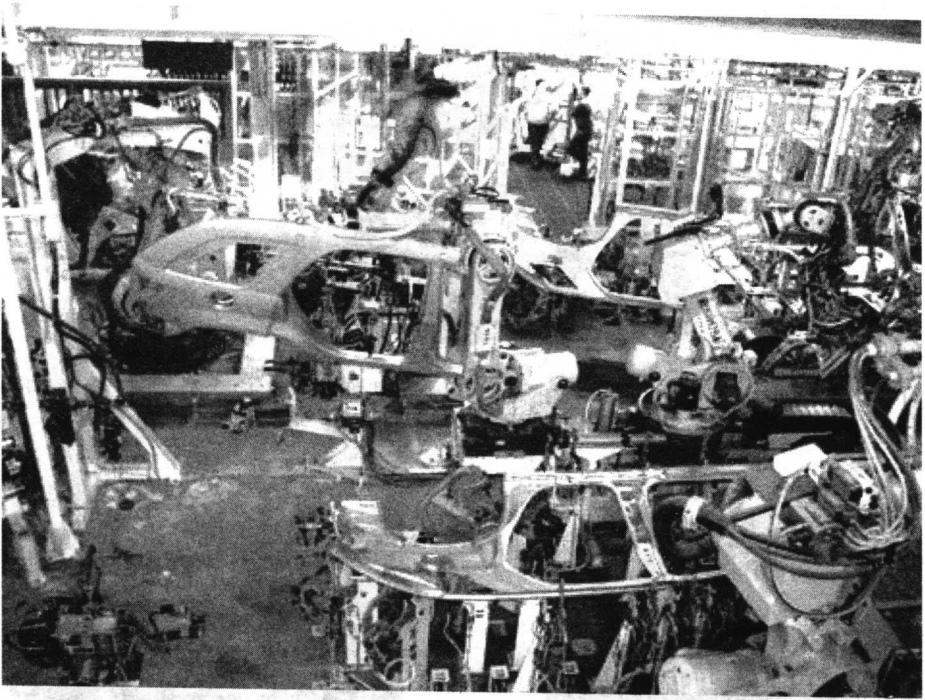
侧围的焊接机器人工位（美国 GM）
